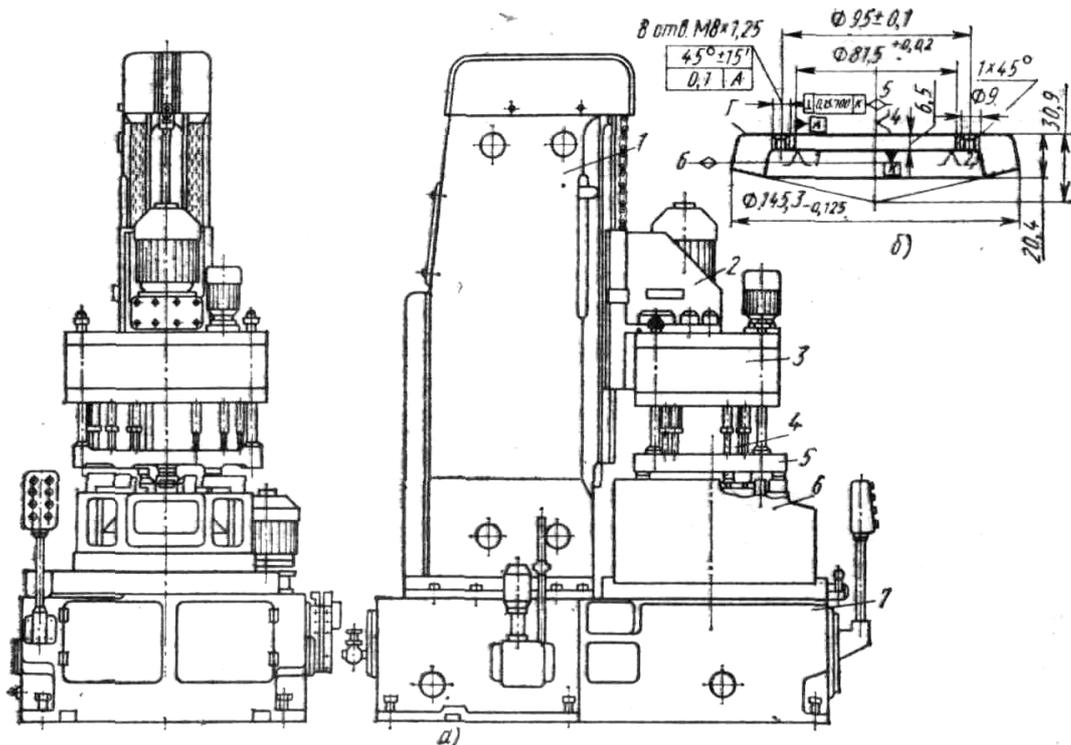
24-шпindelный вертикальный сверлильно-резьбонарезной агрегатный станок:
